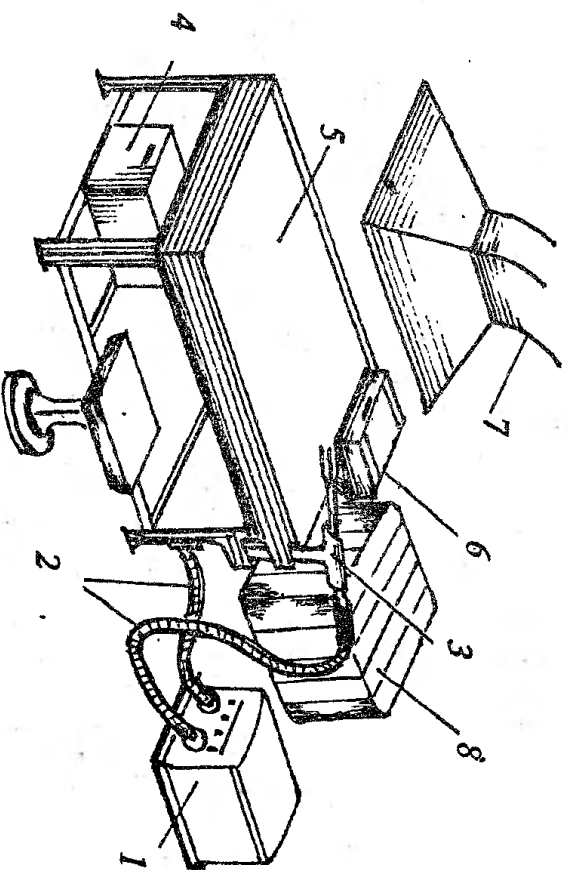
Рабочее место сварщика (луженая сварка).
